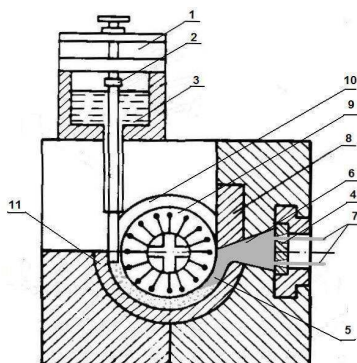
Схема процесса непрерывного прессования Конформ-Кастэкс полых профилей из жидкого металла: 1 – дозатор; 2 – устройство регулирования расхода жидкого металла; 3 – жидкий металл; 4 – матрица; 5 – фронт кристаллизации; 6 – камера сварки; 7 – полые профили; 8 – упор; 9 – колесо; 10 – кольцевая канавка; 11 – кольцевая вставка
